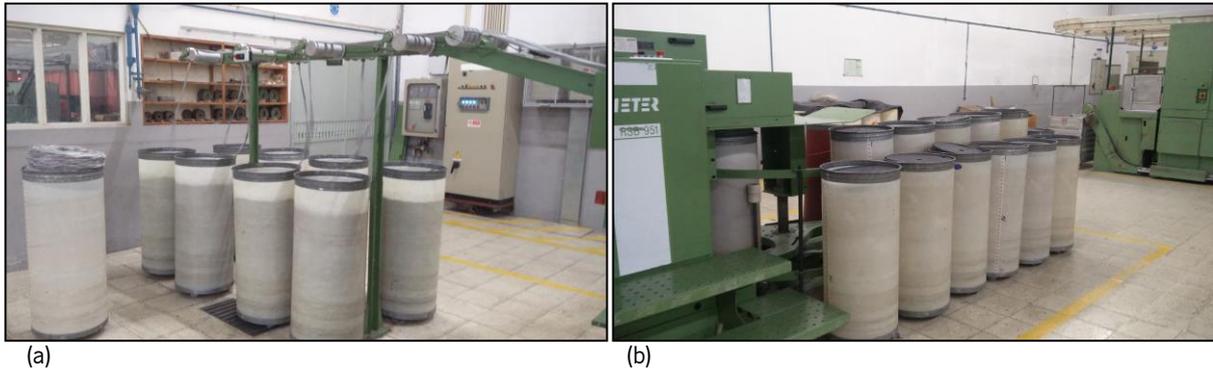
(a) Laminador - vista retaguarda; (b) Laminador - vista frontal.
